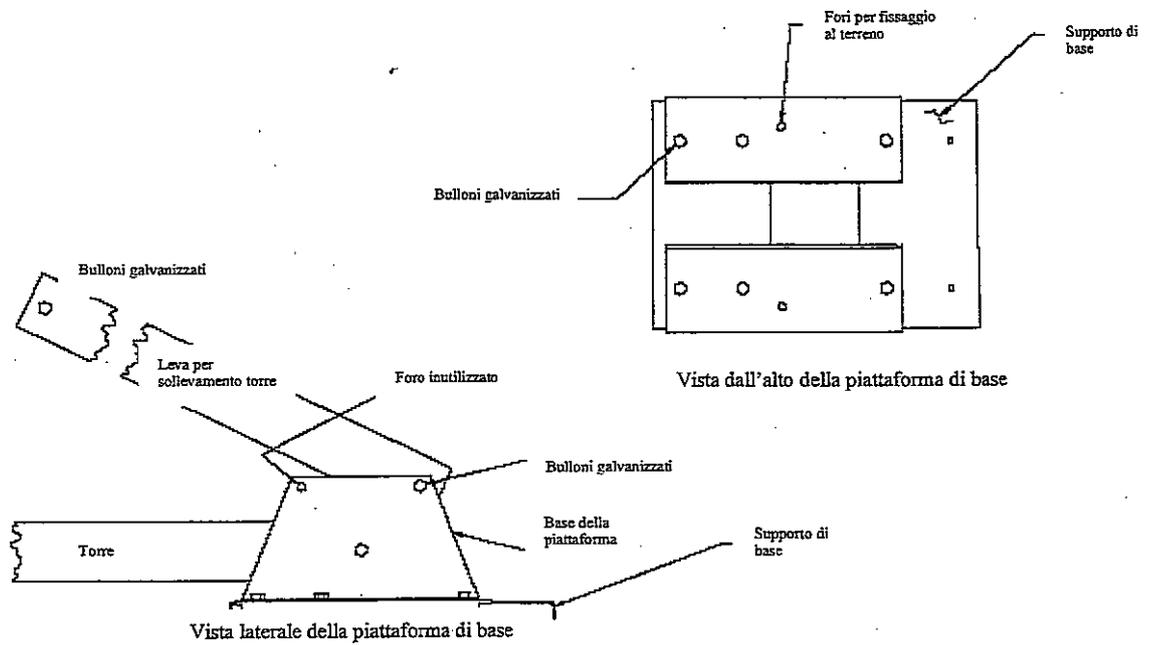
Schema di assemblaggio della Base per l'ancoraggio e sollevamento del palo.
